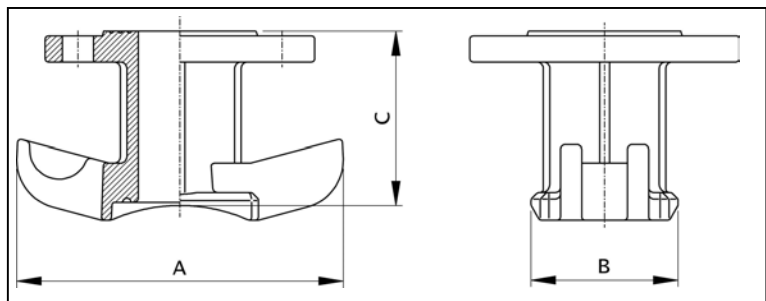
Universal-Anbohrschelle mit Flansch-Abgang DN 40/50 PN 4 (Gas) / PN 16 (Wasser)
